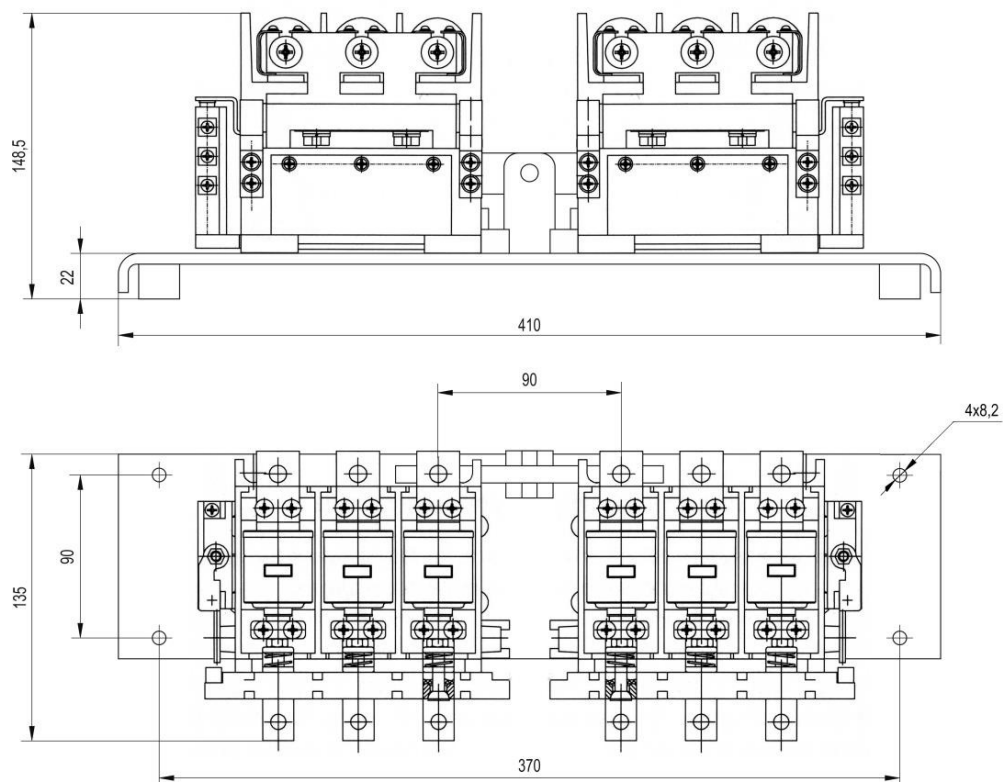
Габаритные размеры КВТ(Р)-1,14-80/125/160
